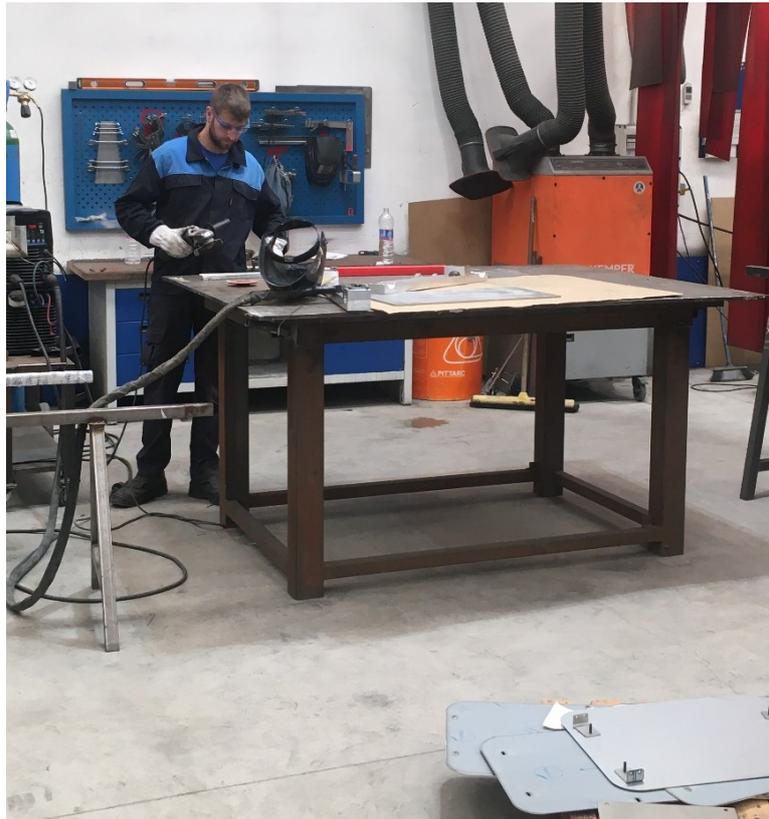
Operario en zona de soldadura y lijado
